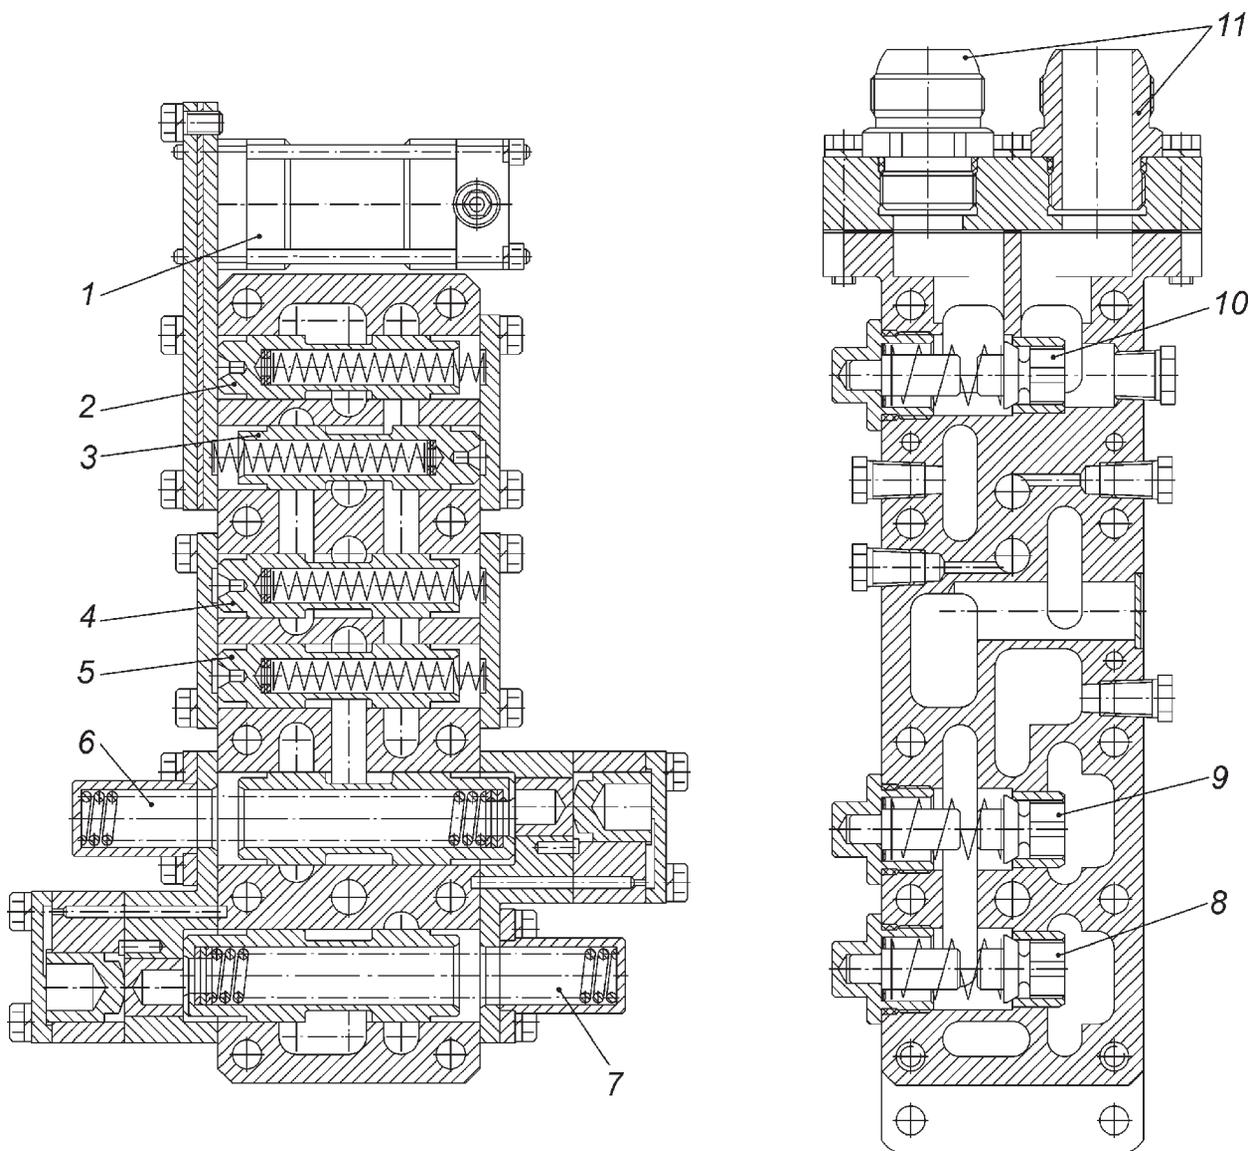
Механизм регулирования давления: 1 — ЭГК блокировки ГДТ; 2 — подпорный клапан; 3 — клапан включения блокировки ГДТ; 4 — клапан смазки; 5 — клапан ограничения входного давления в ГДТ; 6 — клапан главного давления; 7 — клапан отключения переднего насоса; 8 — обратный клапан переднего насоса; 9 — обратный клапан заднего насоса; 10 — перепускной клапан теплообменника; 11 — штуцеры подключения теплообменника
